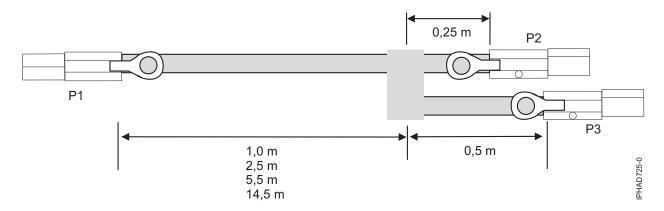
Comprimentos de cabo do conjunto de cabos YO externos SAS
